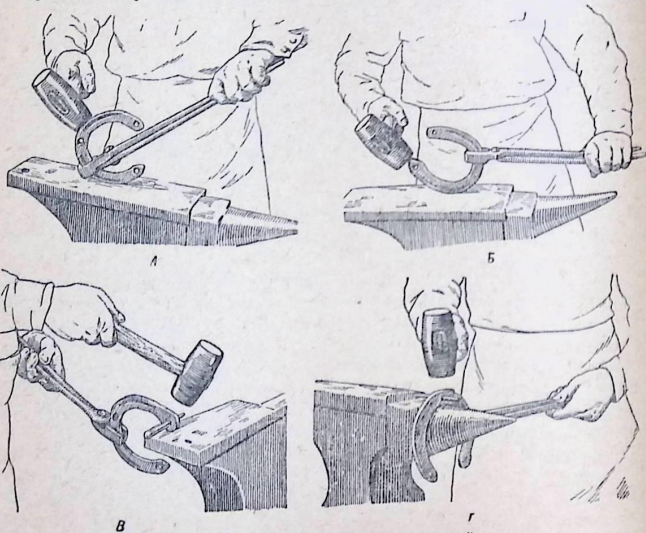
Висадка и оправка шиповых отверстий в подкове:
